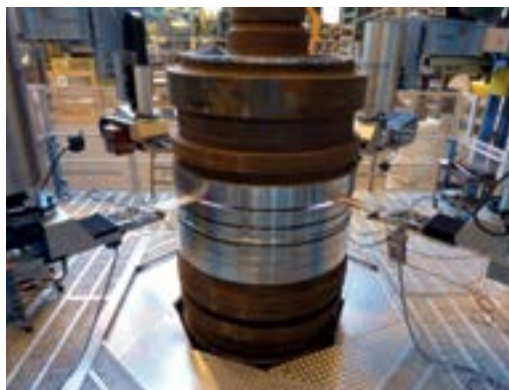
Сварка двумя горелками. (нижний проход – одной горелкой, верхний проход – второй на 180°). Этим методом возможна сварка без остановок, исключаются угловые смещения (баланс напряжения усадки)
